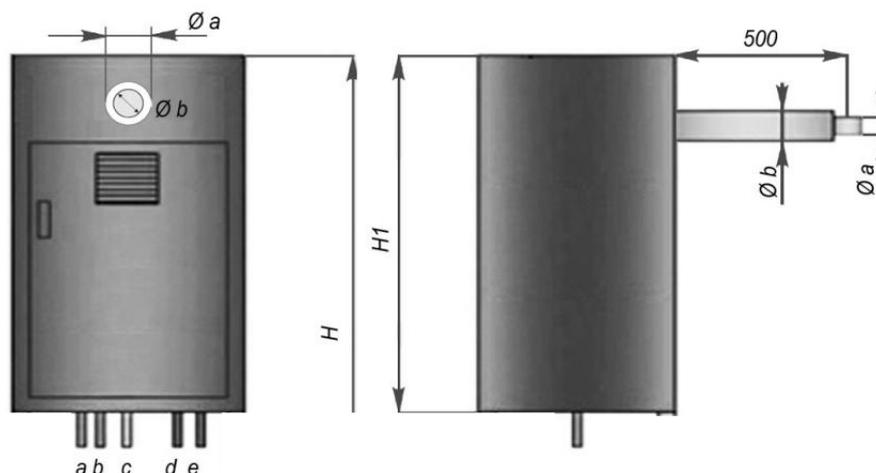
Габаритные размеры бокса для котлов наружного размещения
